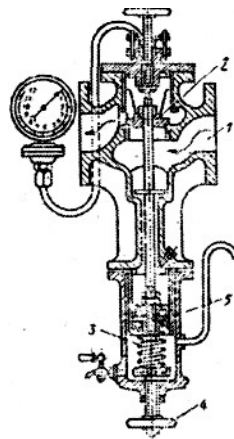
Редуційний клапан: 1 — канал; 2 — золотник; 3 — пружина;
